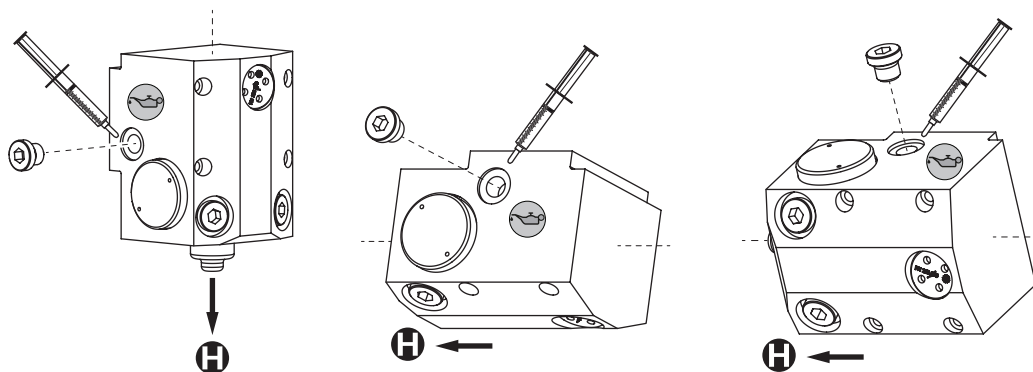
La posizione delle viti del dispositivo di riempimento dipende dall'orientamento di montaggio. Esempio: Versioni U
